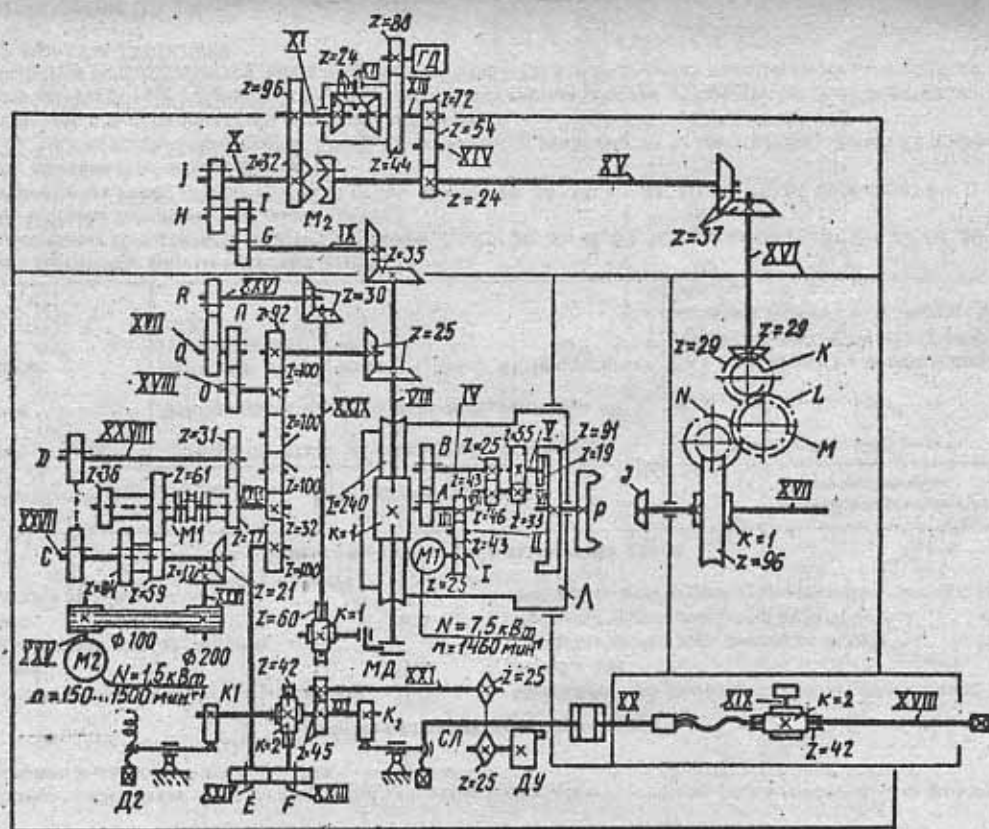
Кинематическая схема зуборезного станка мод. 5С280П
